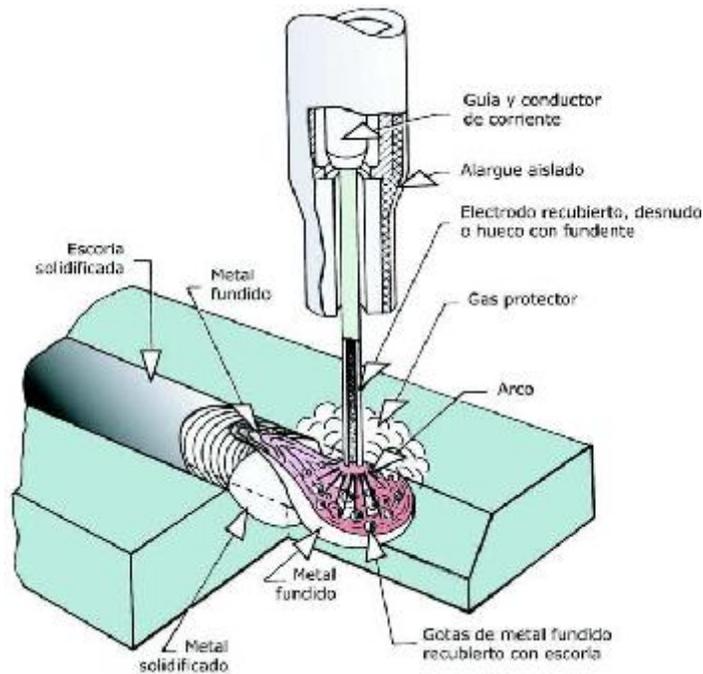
Soldadura por arco con núcleo de fundente protegida con gas.
